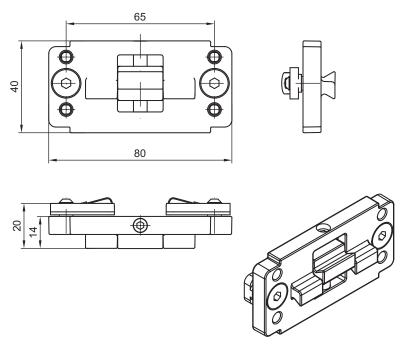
Supporto di serraggio BT-P40 per il fissaggio nelle colonne di fissaggio UDC
